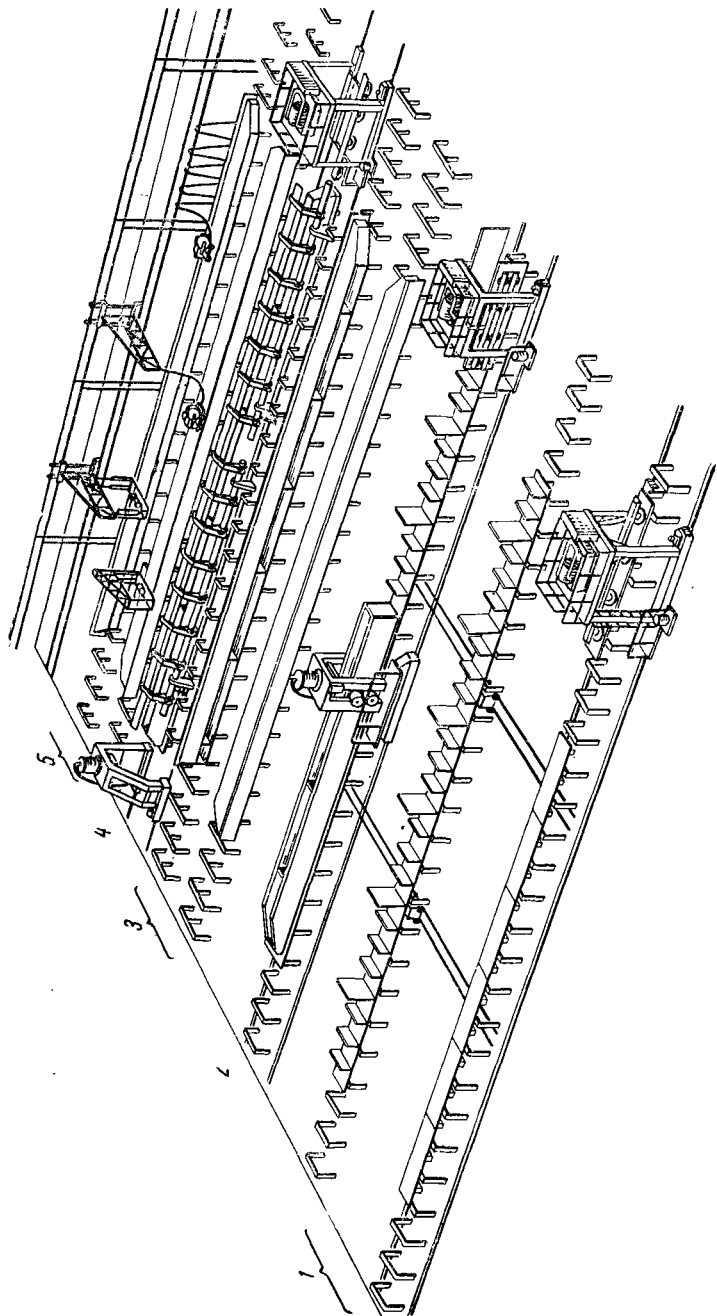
Общий вид сборочно-сварочного участка изготовления балок мостовых кранов
